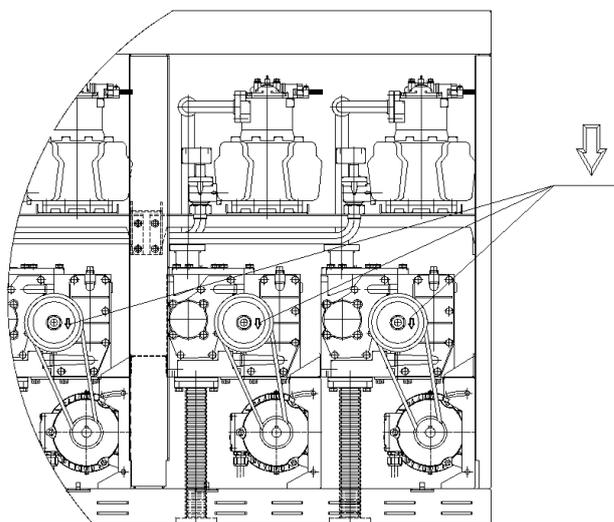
Проверка направления вращения ротора двигателя насоса (стрелка)
